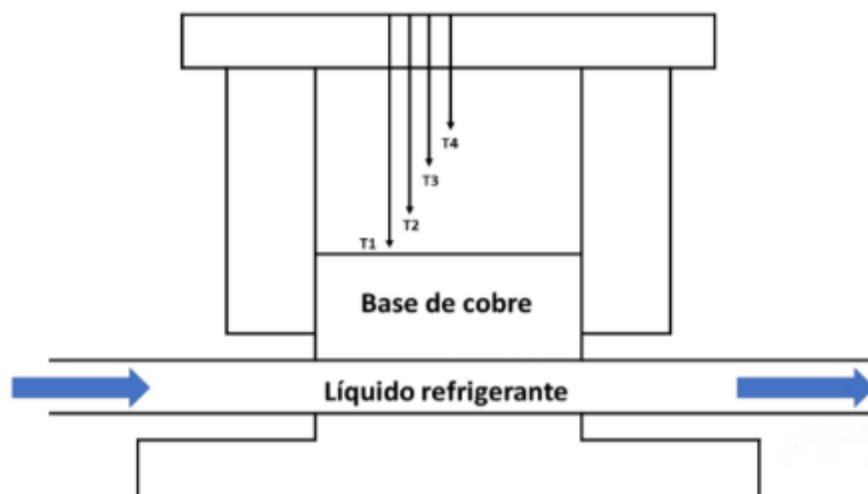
Esquema del molde utilizado para la solidificación. [32]
